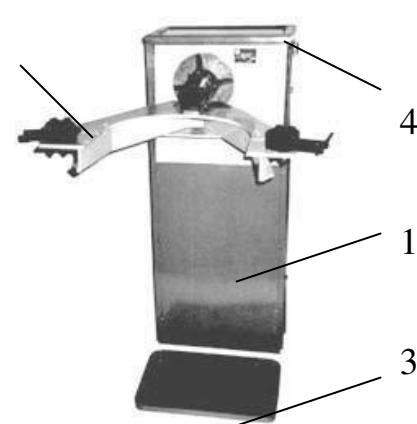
Стенд для разборки и сборки двигателей Р-640: 1 – корпус; 2 – поворотный стол; 3 – поддон; 4 – пульт управления.
